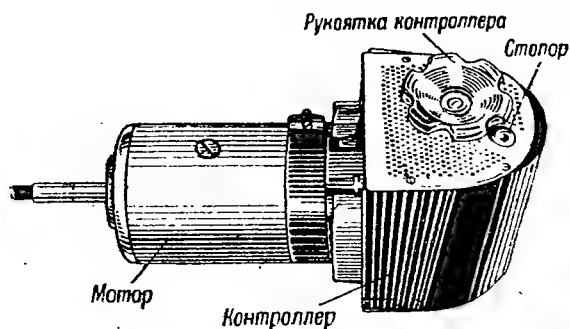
Внешний вид мотора поворота башни в сборе с контроллером на танке Т-34
